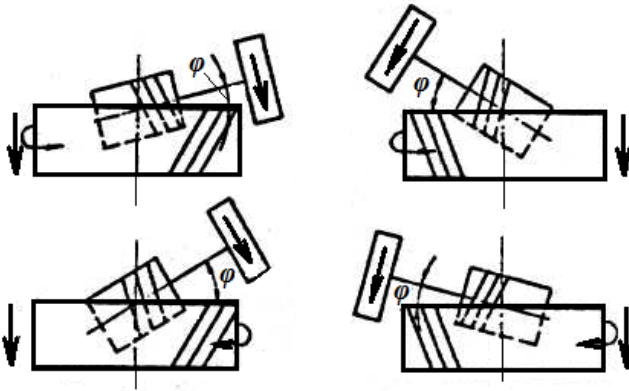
Схеми установлення черв'ячної фрези
